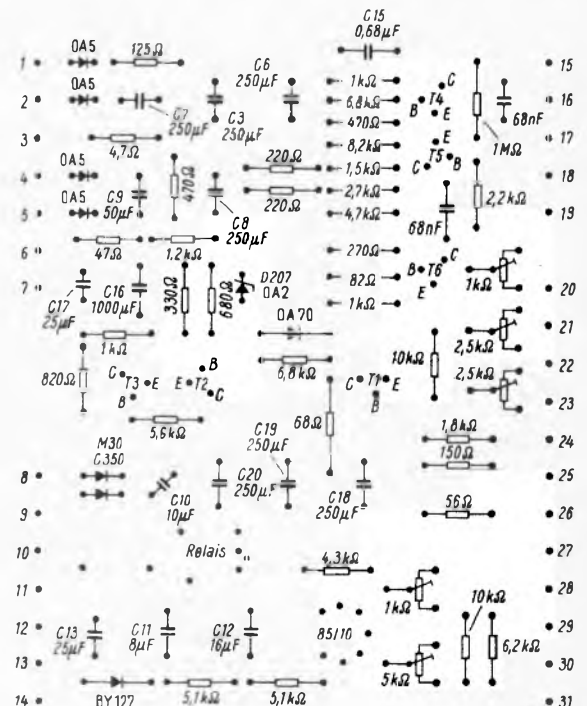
Lageplan der Bauelemente auf der nach Bild 11 hergestellten Platine (Maßstab 1 : 2)
